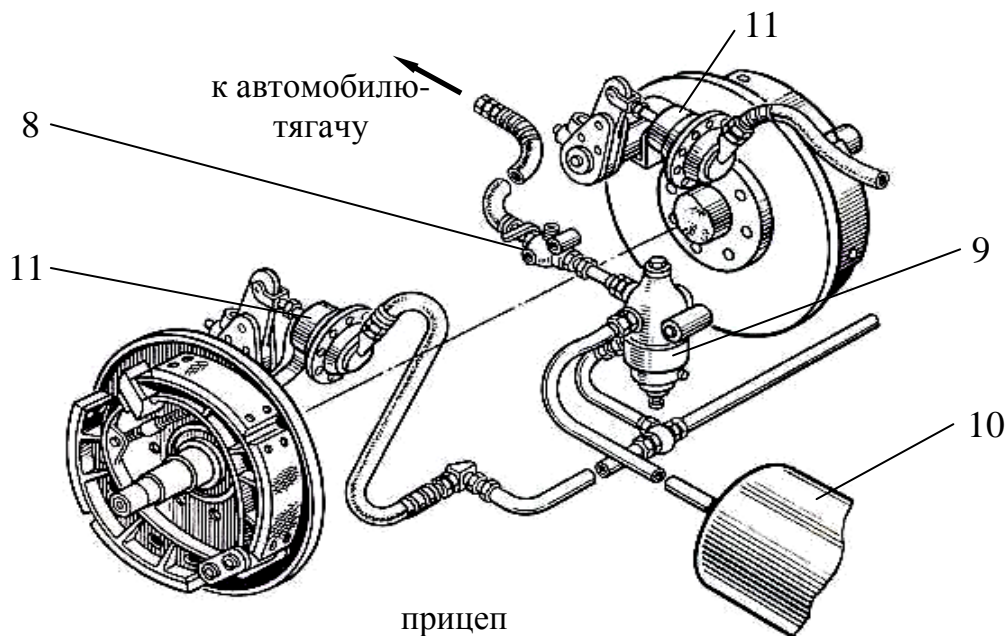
Компоновка элементов тормозного привода на прицепе при однопроводном приводе: 8 – соединительная головка; 9 – воздухораспределитель; 10 – ресиверы прицепа; 11 – тормозные камеры колес прицепа
